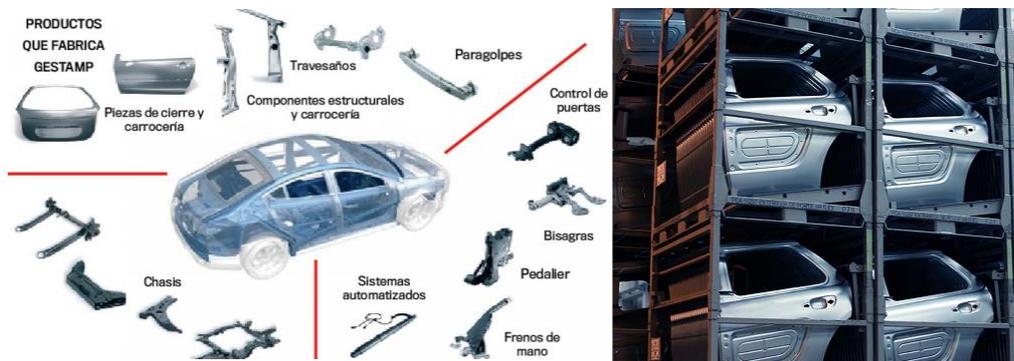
Diferentes elementos que se ensamblan en el proceso de fabricación de los automóviles.
